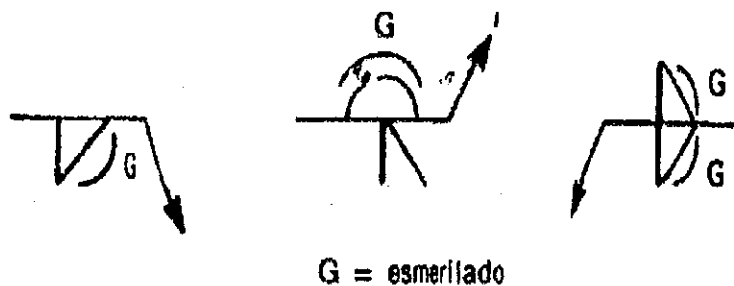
Símbolos de acabado para soldaduras acabadas mecánicamente, de cara plana.
